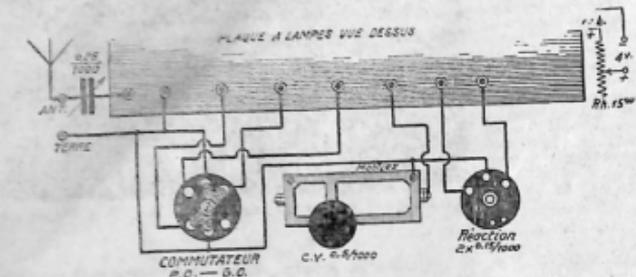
Assemblage du panneau frontal et de la plaque à lampes vue dessus.
